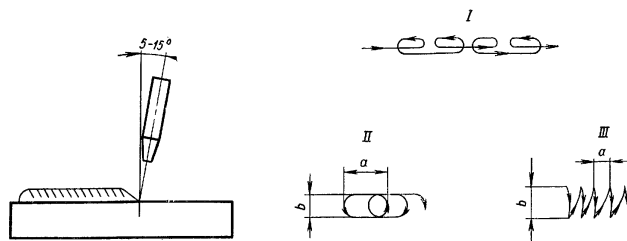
Схемы перемещения горелки при полуавтоматической сварке стыковых швов в среде защитных газов:
